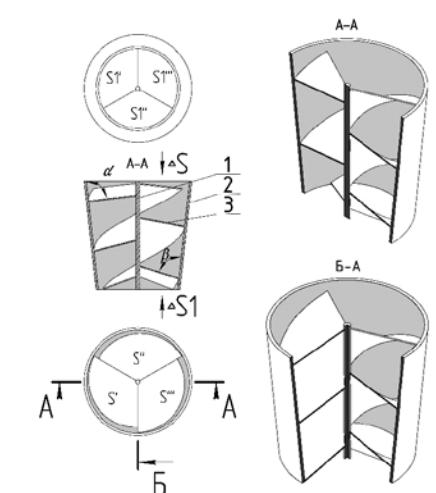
Турбіна з прямими спіралеподібними лопатями та звуженням корпусу (1 – вал, 2 – порожнистий циліндричний корпус, 3 – спіралеподібна лопать)
